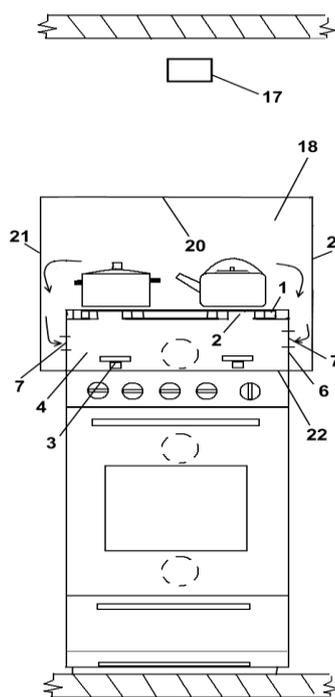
Конструкция бытовой газовой плиты: вид спереди
